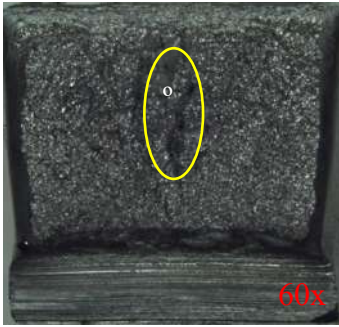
Vista macroscópica de la fractura, 22MnB5, -18°C, condición 1.
